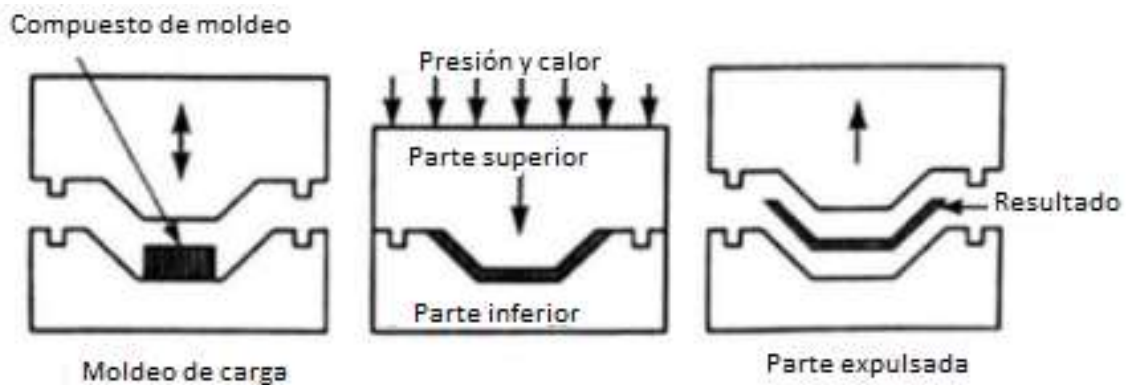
Esquema del equipo de conformado por molde a compresión. [15]
